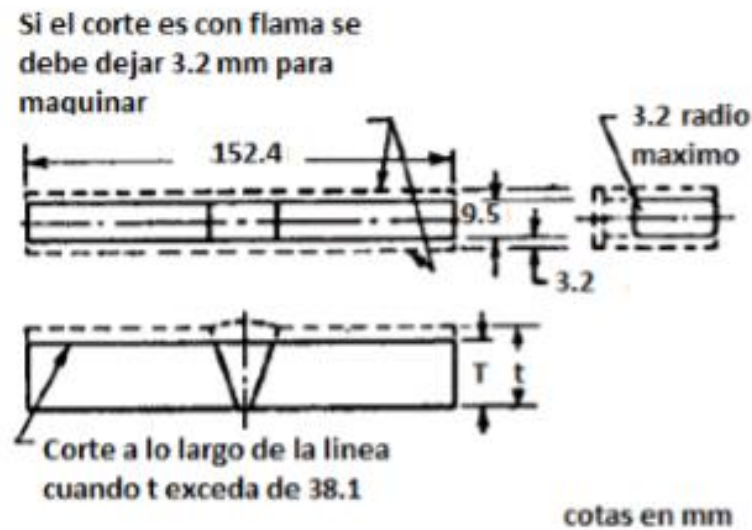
Soldadura transversal de probeta [21]
